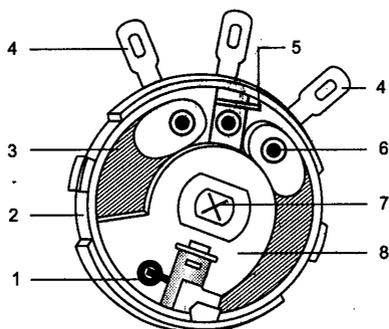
Переменный непроволочный резистор (1 - токосъемник; 2 - пластмассовый круглый корпус; 3 - токопроводящий элемент; 4 - внешние выводы; 5 - стопор; 6 - заклепки; 7 - вращающаяся ось с торцом; 8 - изоляционная планка)
